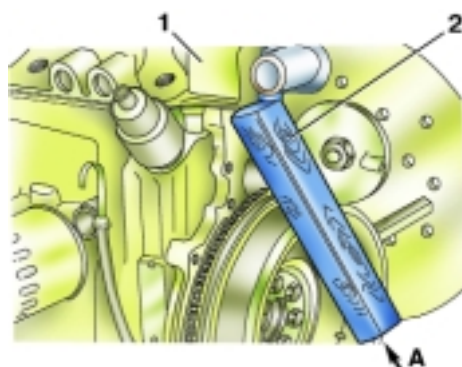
Снятие головки блока двигателя F3R 272: 1 – головка блока; 2 – деревянный брусок
